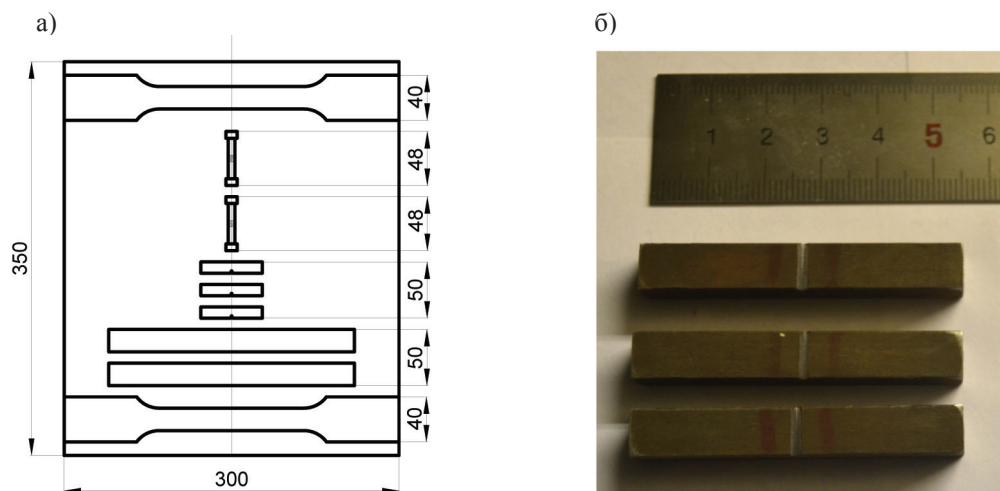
Образцы для испытаний на ударную вязкость: схема вырезки (а); фотографии образцов (б)
